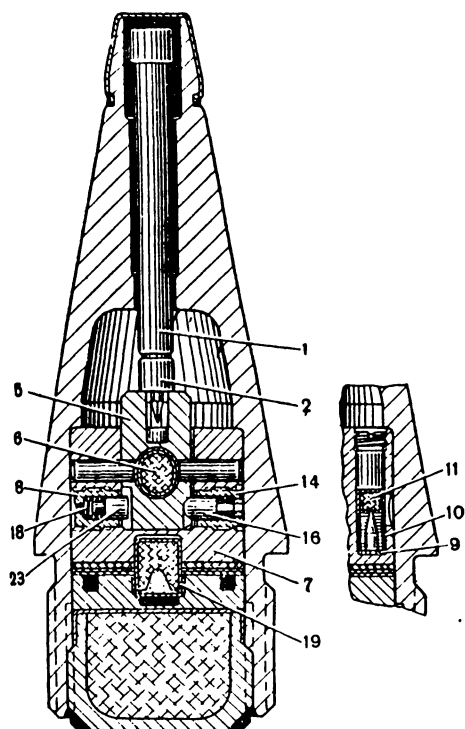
Взрыватель А-37. Положение деталей при выстреле:
